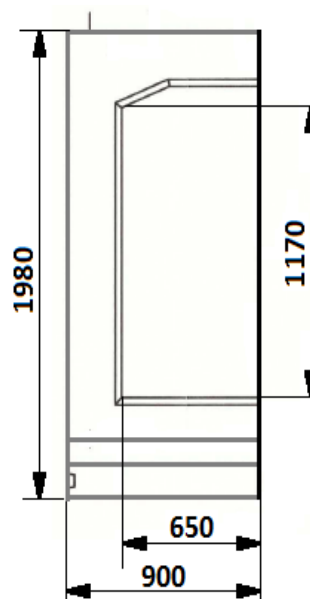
Внешний вид и размеры блока «СБ-2-1».
